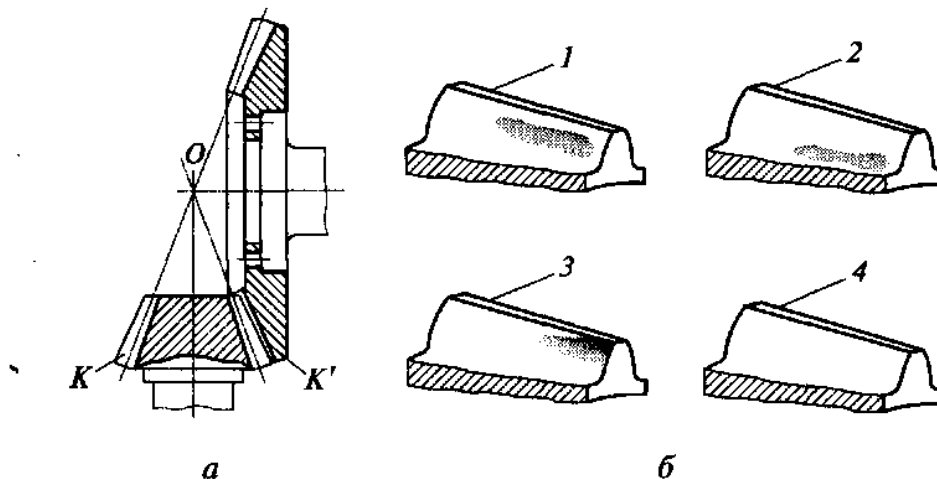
Регулировка зацепления зубьев колес (а) и отпечатки краски при проверке качества зацепления (б) конической зубчатой передачи:
